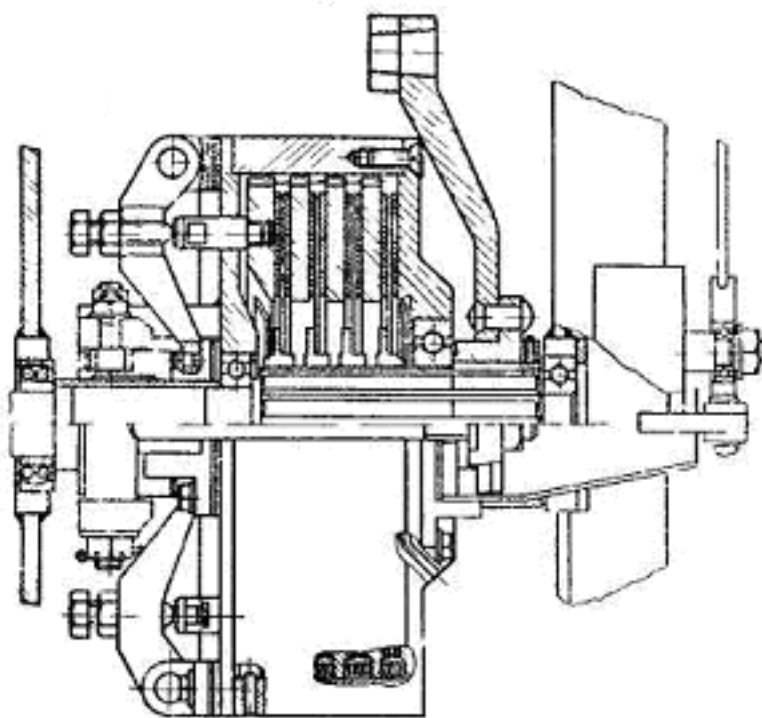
Стенд для испытания рулевого механизма ленточным тормозом
